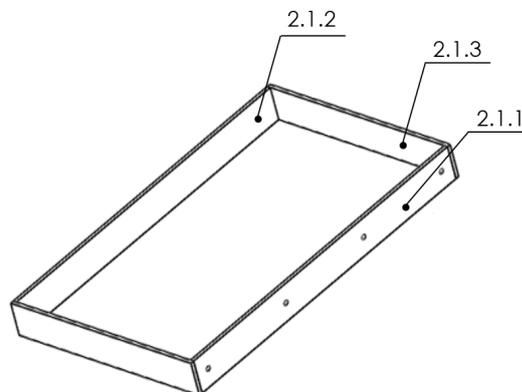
Ensamblaje subconjunto 2.1 mesa de centro. Soldadura 3
